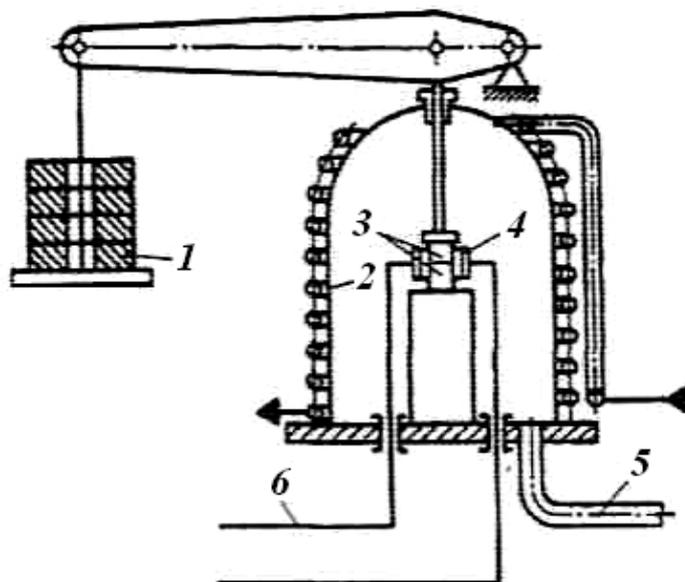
Схема диффузионной сварки в вакууме:
